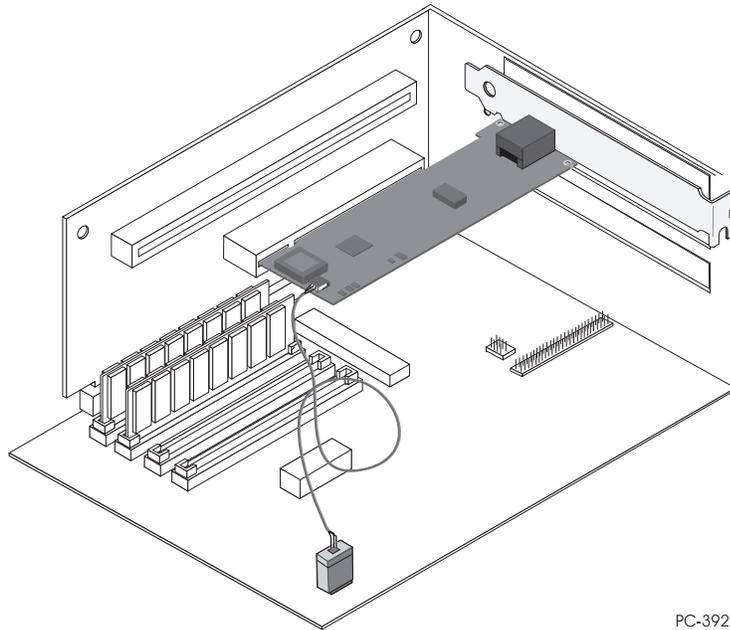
Kabel mit zwei Steckern für Wake On LAN anschließen
